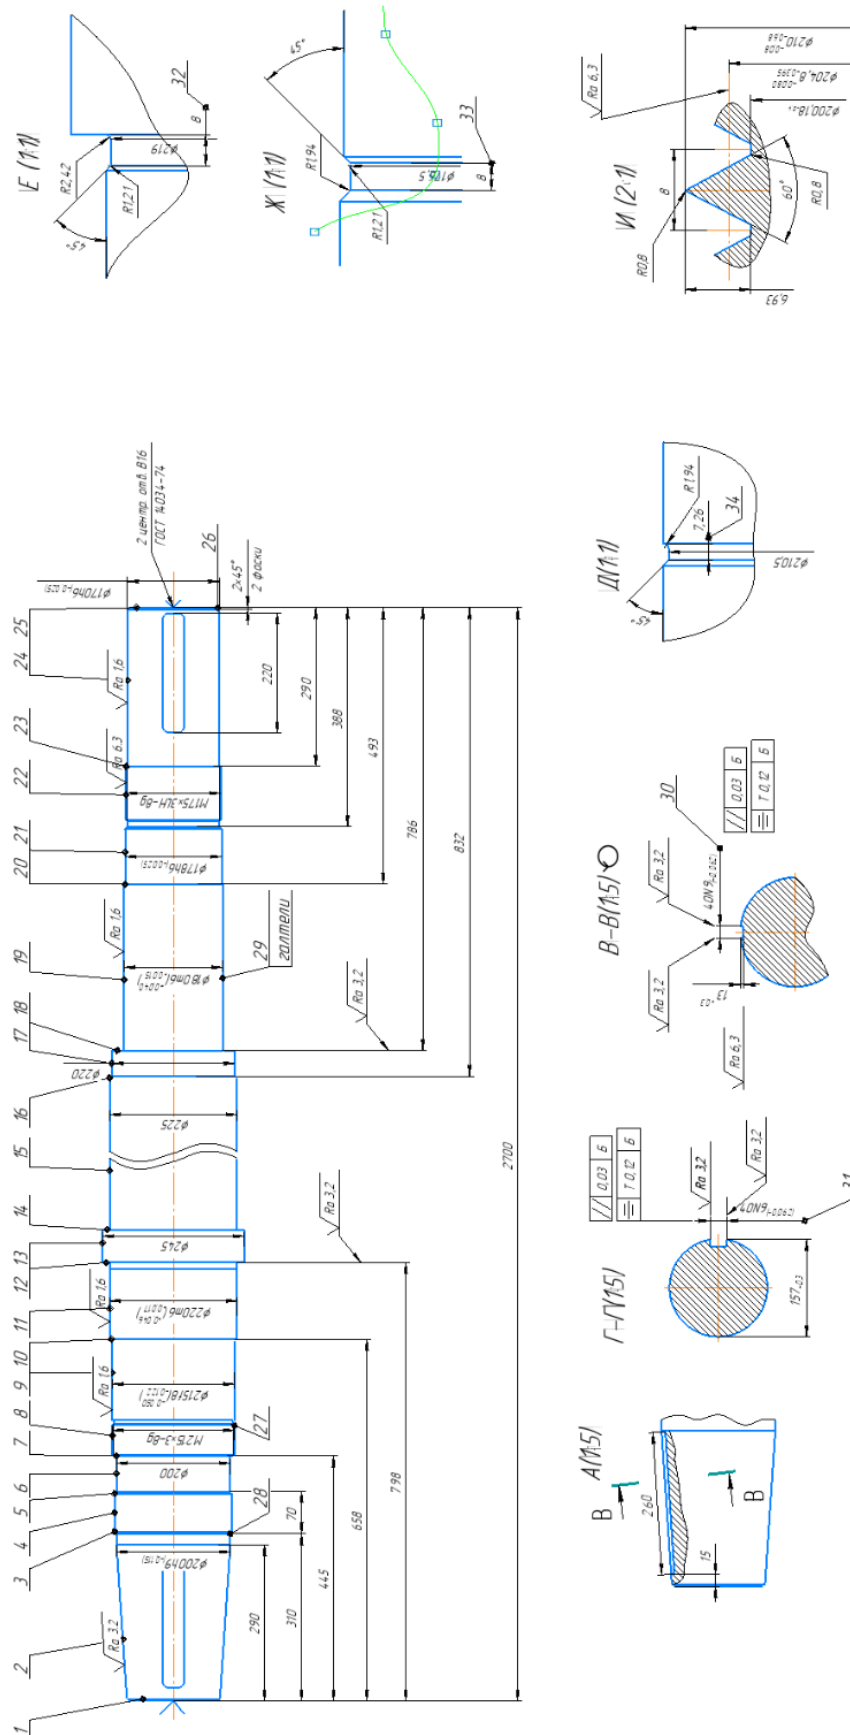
Нумерація поверхонь деталі «Вал»
